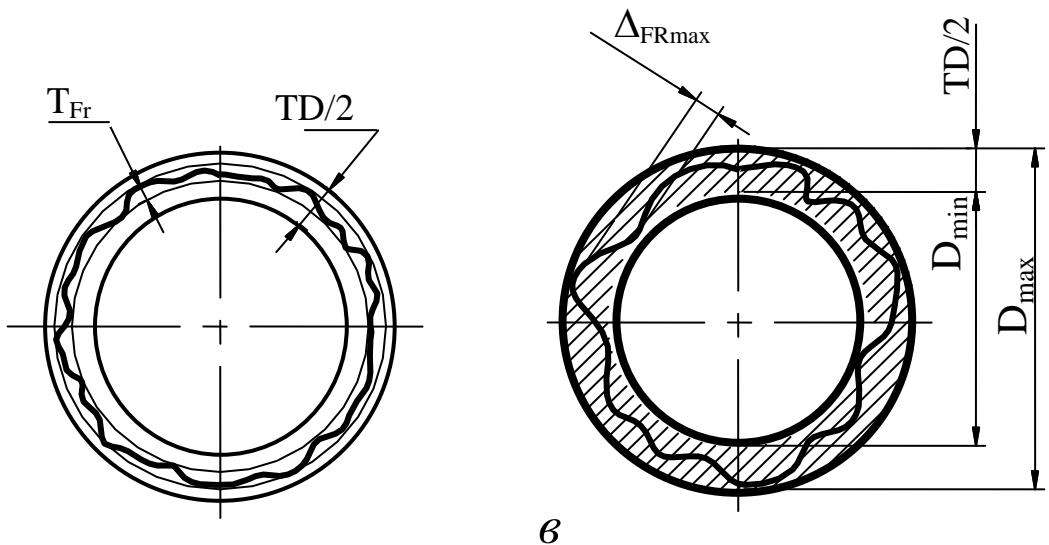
Допуски конусів, установлені ГОСТ 8908-81
